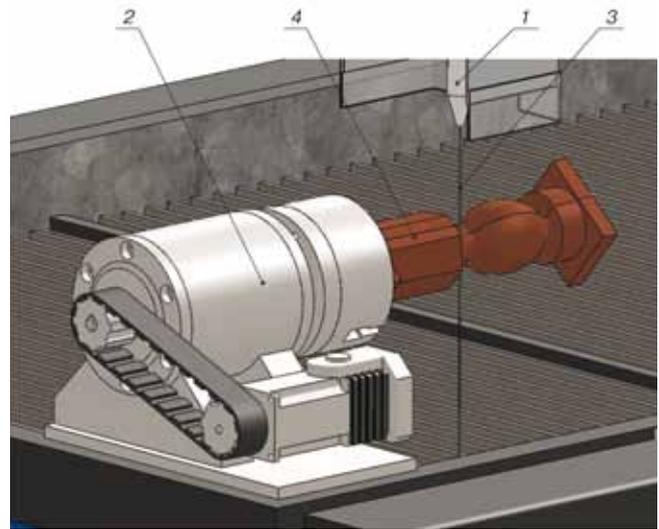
Процесс токарно-гидроабразивной обработки двух деталей: 1 – режущая головка ГАР; 2 – поворотная головка; 3 – режущая струя; 4 – заготовка.
